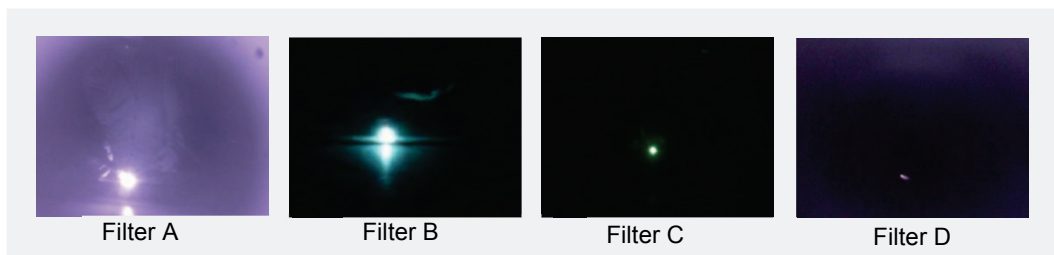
Filter A Tageslichtsperrfilter (750 nm), Filter B Schweißglas Schutzstufe 9, Filter C Schweißglas Schutzstufe 10, Filter D Tageslichtsperrfilter (850 nm) + Schweißglas Schutzstufe 9.
